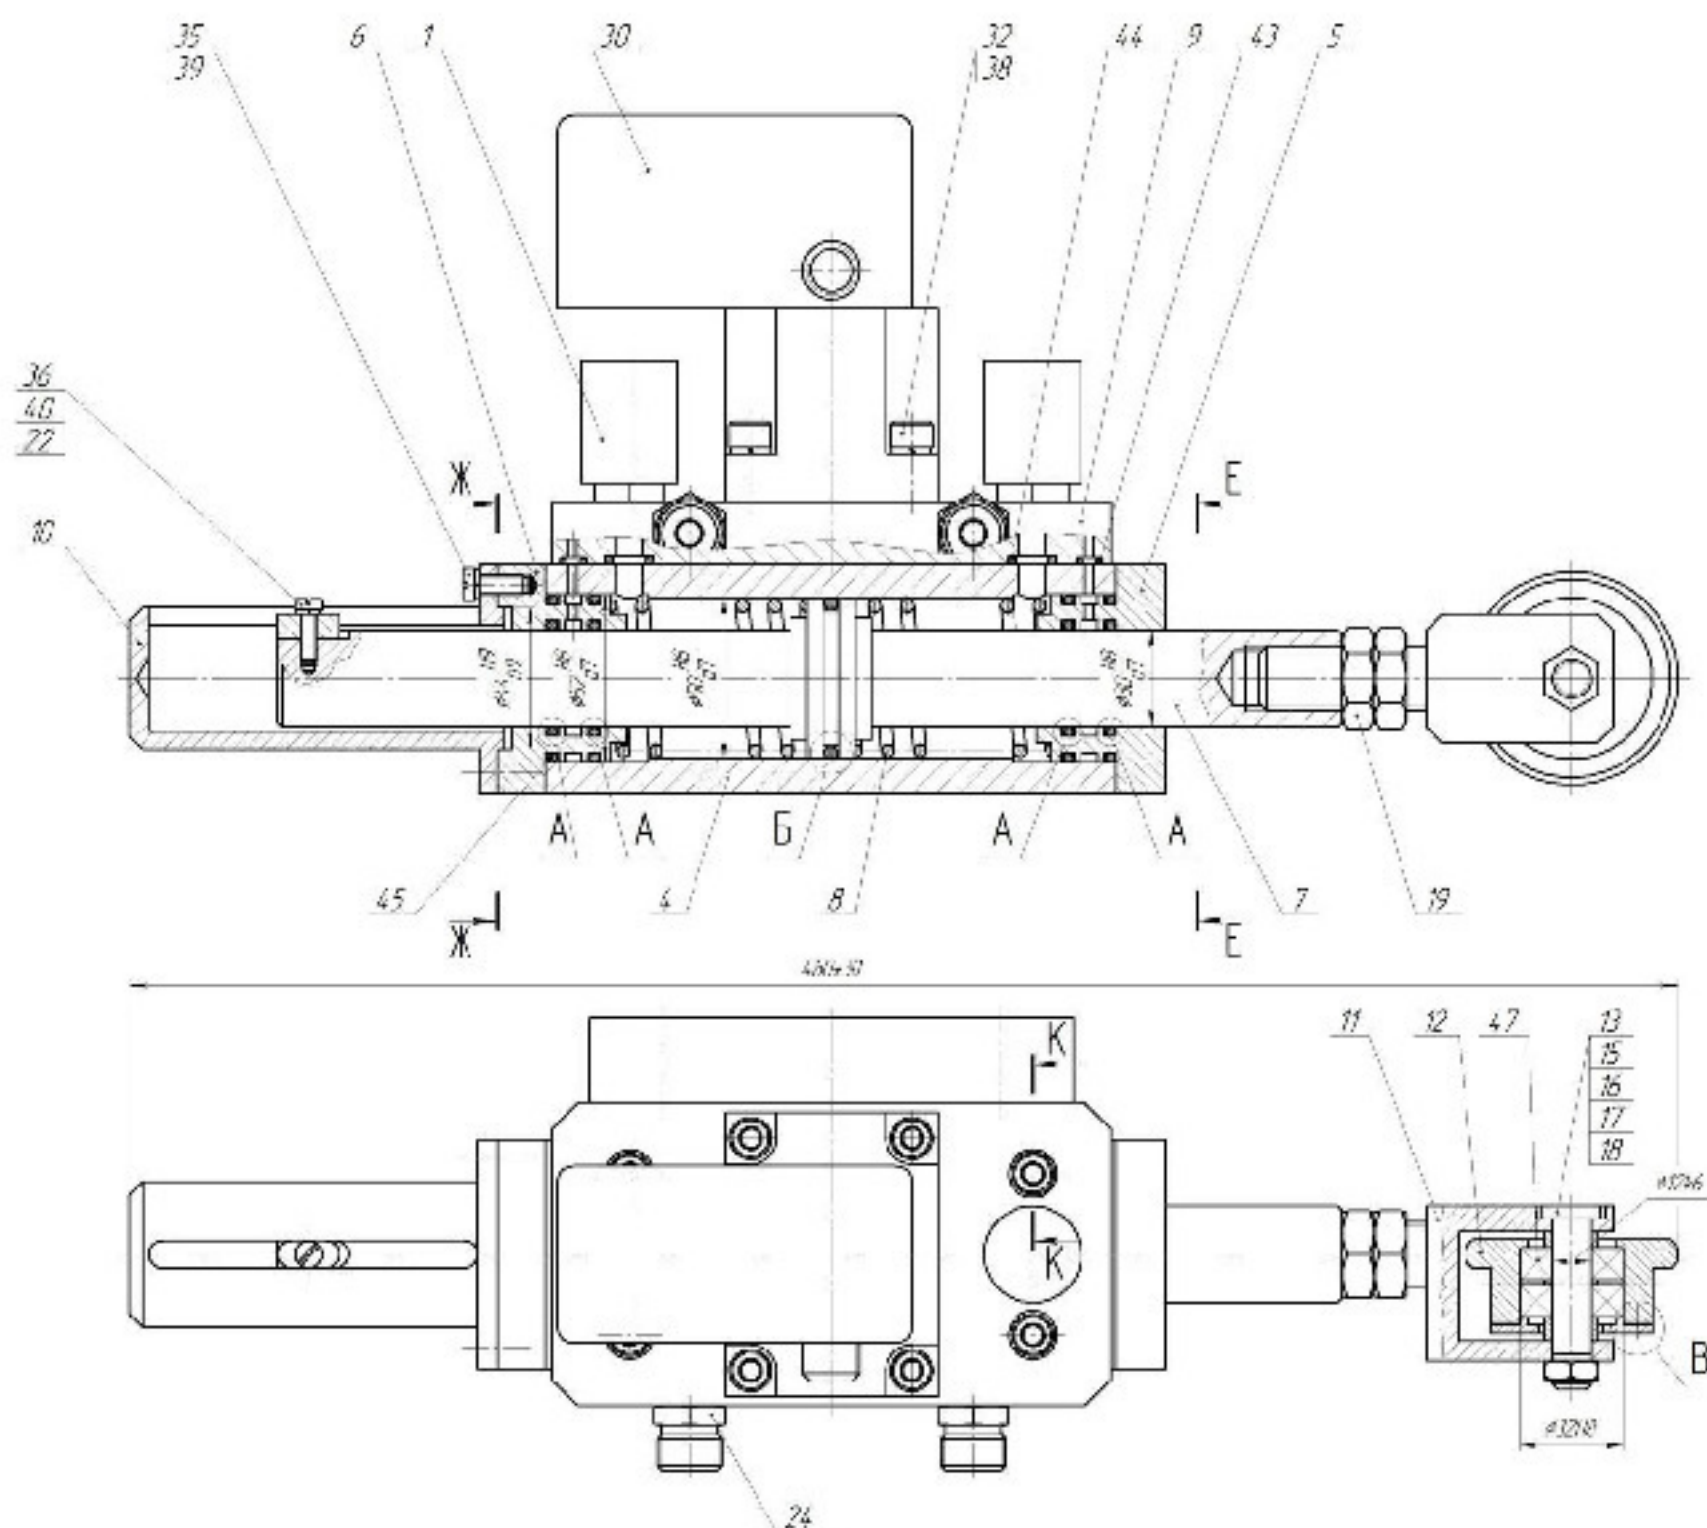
Конструкція пристрою з ЕГСП для обкочування нециліндричних заготовок
